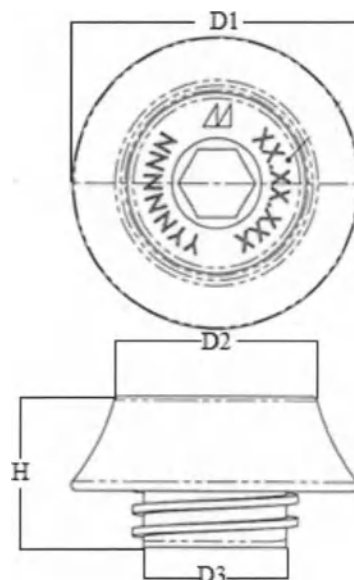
Винт с шайбой для стяжки поперечной MUST MINI;
